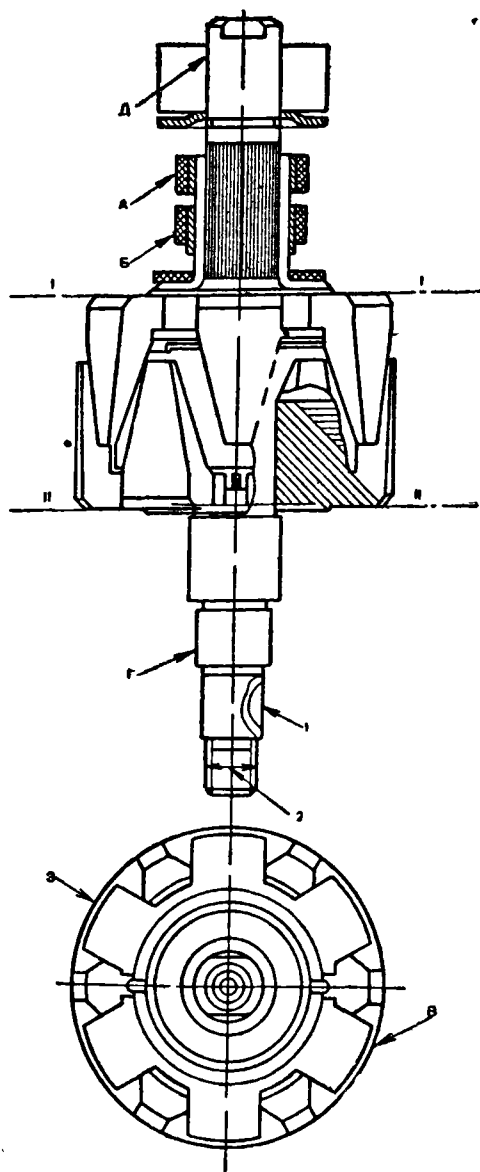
Ротор генератора Г-424 в сборе: 1 — шпоночный паз; 2 — резьба вала; 3 — обмотка
